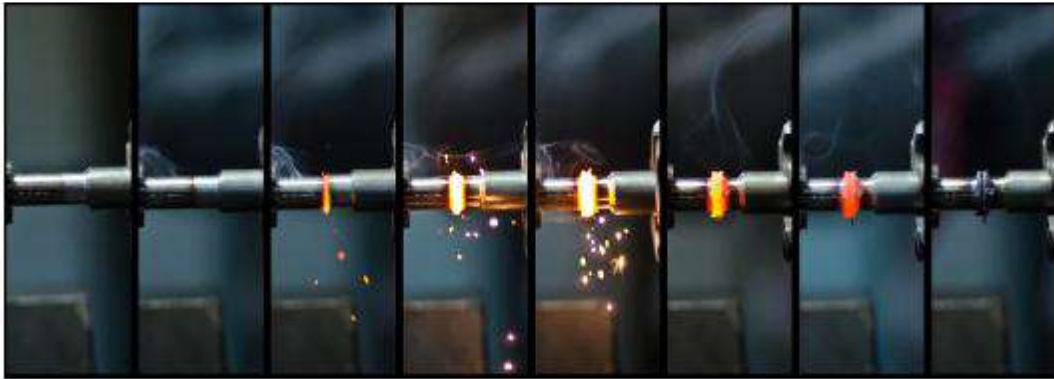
Principios de la soldadura por fricción. Fuente: Ptak (2010).
